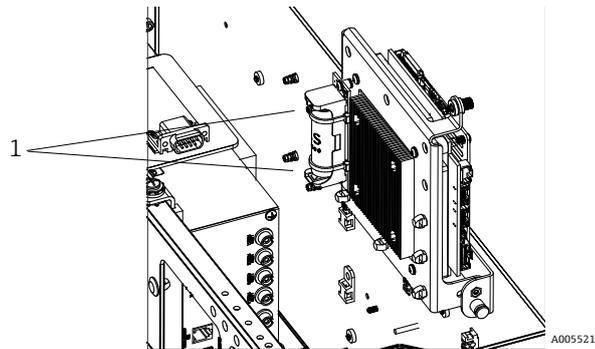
Kabelbinder, mit denen die Batterie gehalten wird, entfernen
